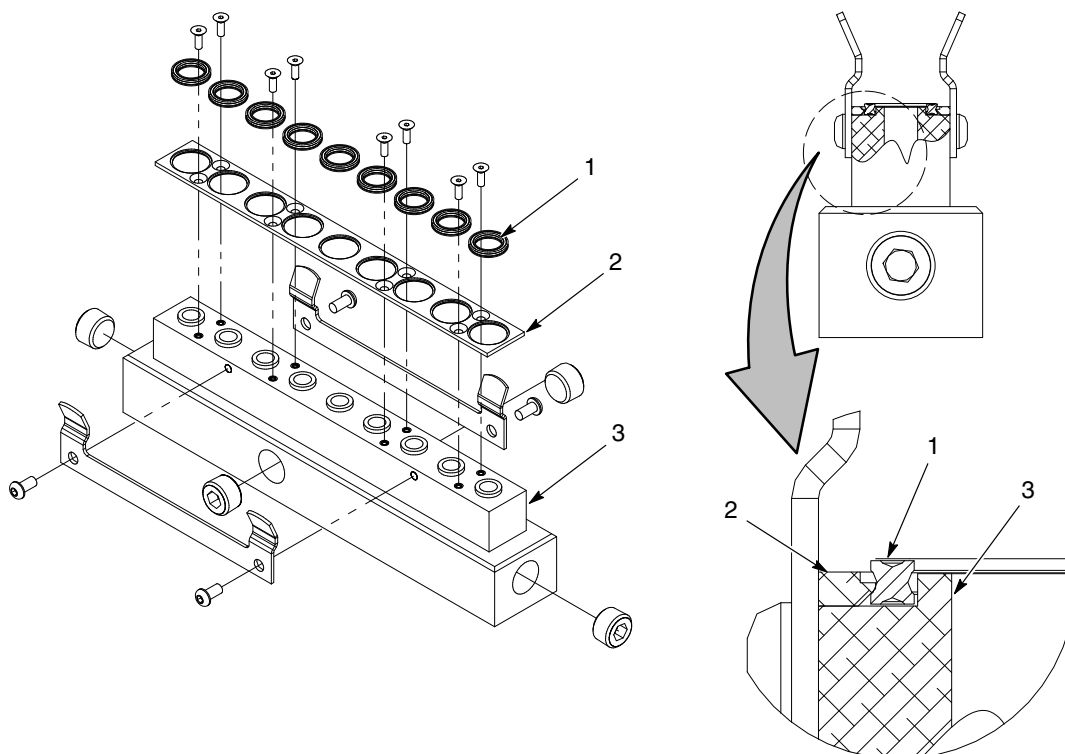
Quad-Ring am Spülverteilerblock ersetzen
